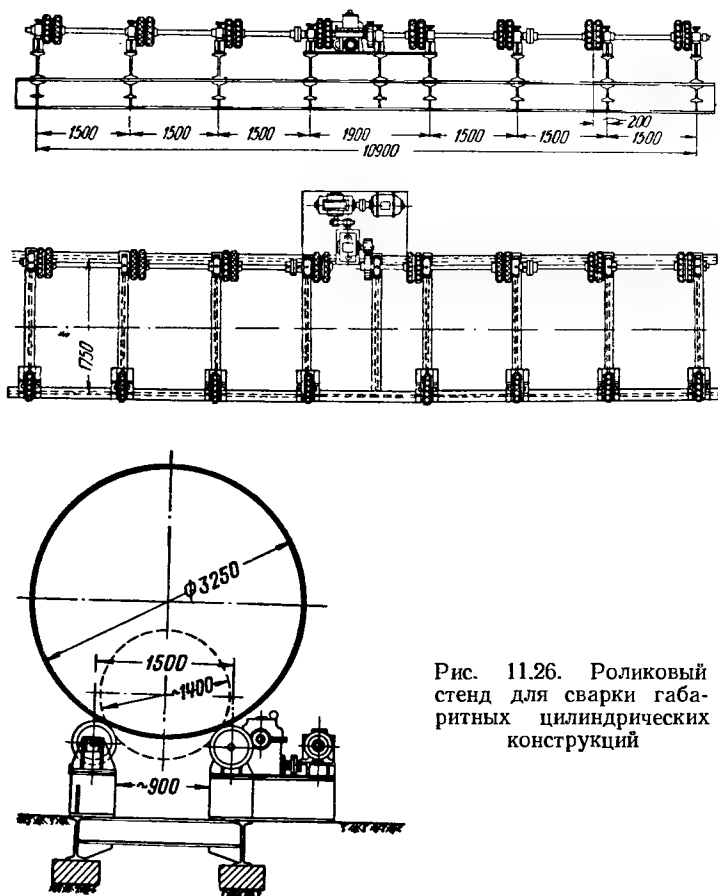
Роликовый стэнд для сварки габаритных цилиндрических конструкций
